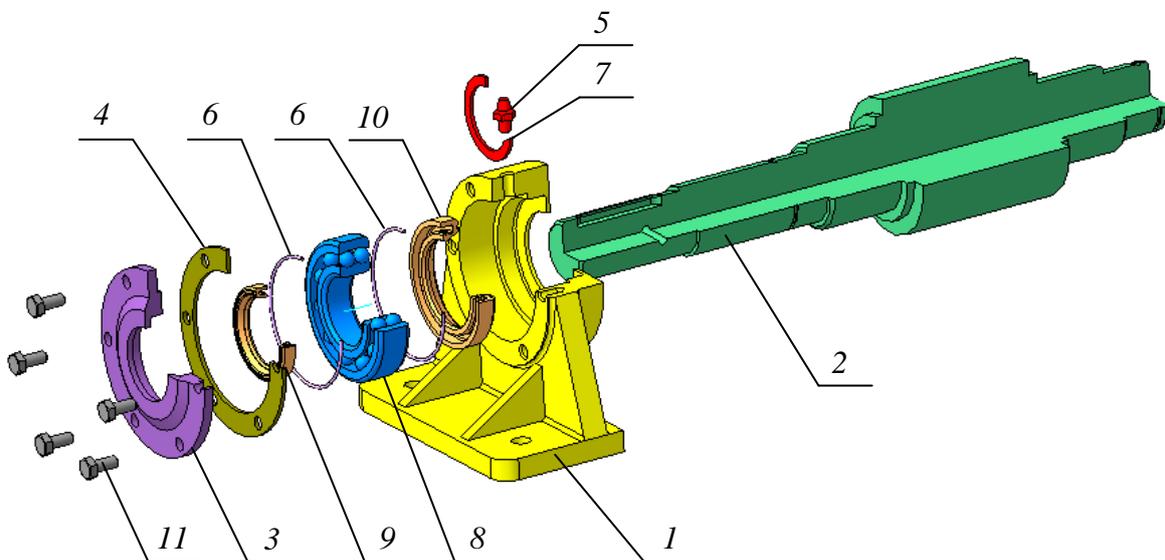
Трехмерная модель сборочного узла «Узел подшипниковый» в разнесенном виде: 1 – корпус; 2 – вал; 3 – крышка; 4 – прокладка; 5 – заглушка; 6 – кольцо уплотнительное (2 шт.); 7 – кольцо упорное; 8 – радиальный шариковый двухрядный подшипник 1207 ГОСТ 28428–90; 9 – манжета 1.1-36×48-1 ГОСТ 8752–79; 10 – манжета 1.1-44×65-1 ГОСТ 6752–79; 11 – болт М6 ×14 ГОСТ 7805–70 (6 шт.)
